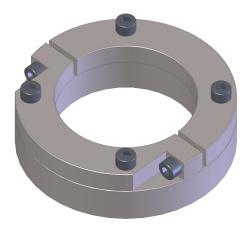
Anello di ritenuta assemblato e montato sulla piastra di fissaggio
